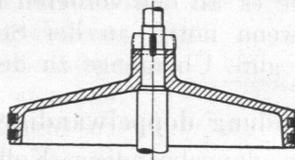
Kolbenbefestigung durch Querkeil (veraltet).
